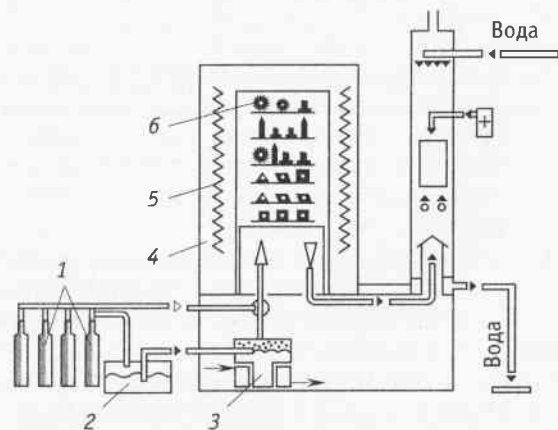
Схема установки для химического осаждения покрытий из газовой фазы на твердосплавный инструмент:
